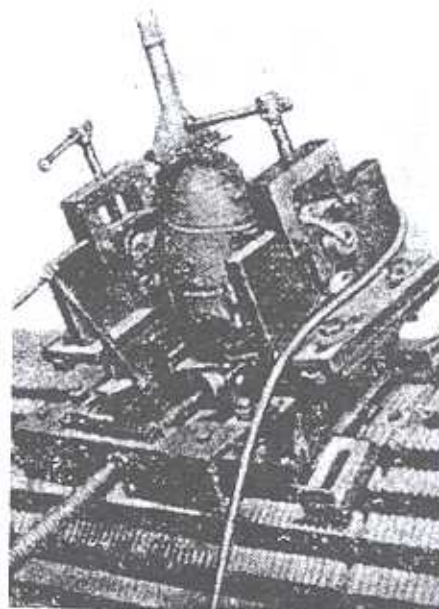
Приспособление для фрезеровки наклонных скосов в зубцах ротора
